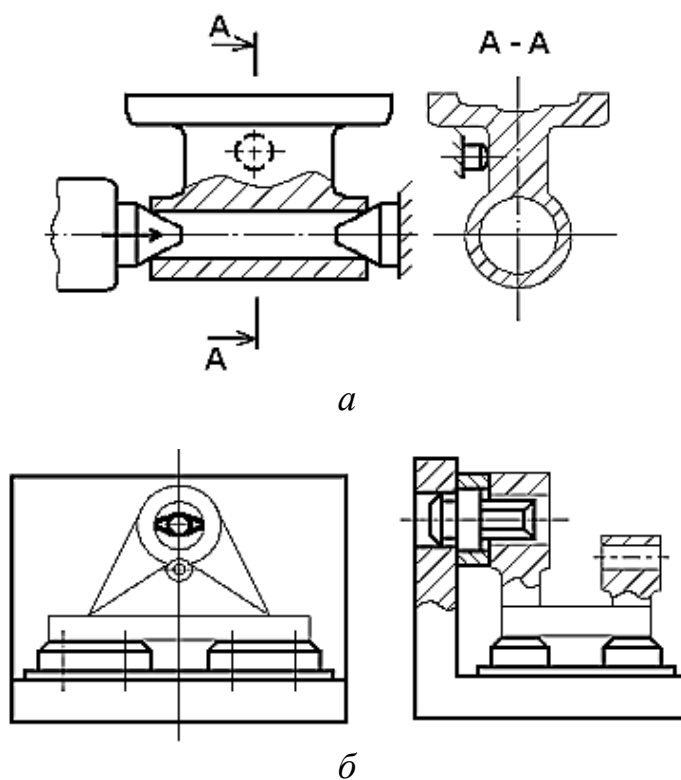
Комбинированные схемы установки корпусных деталей:
